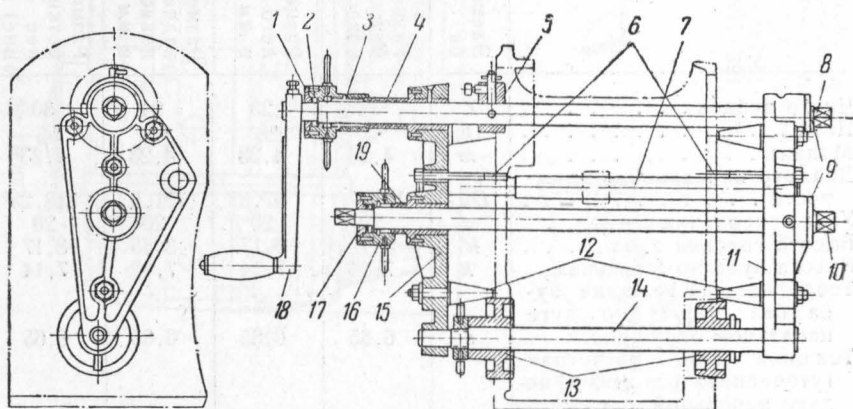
Приспособление для расточки гнезд подшипников в коробке перемены передач:
